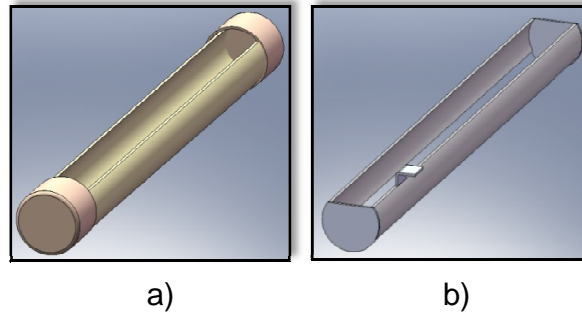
Diseños de la celda de prueba en PVC: a) Diseño de la celda y b) Diseño del cátodo.
